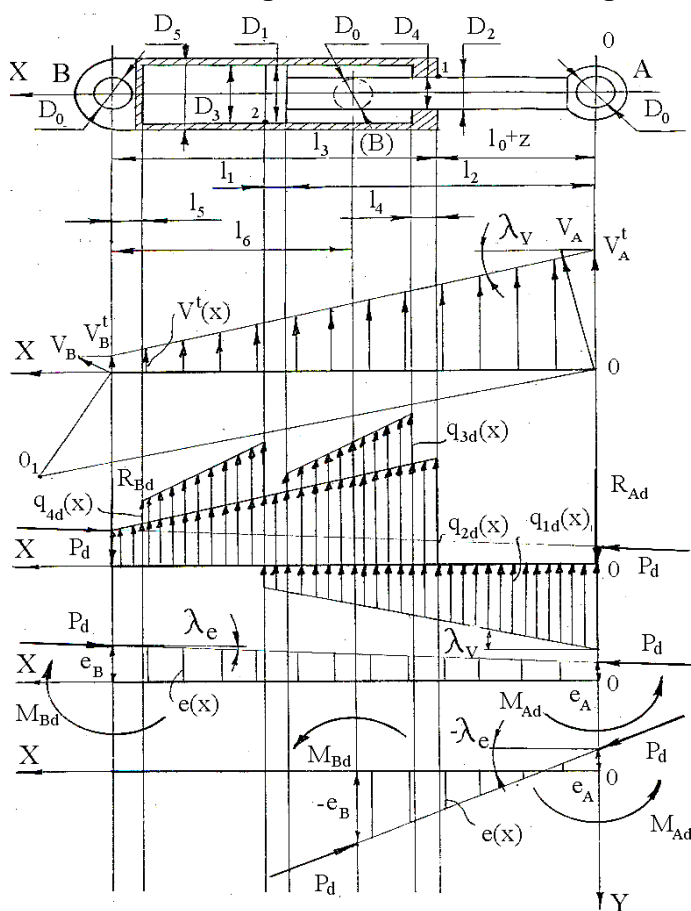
Расчётная схема нагружения гидроцилиндра динамической нагрузкой.
